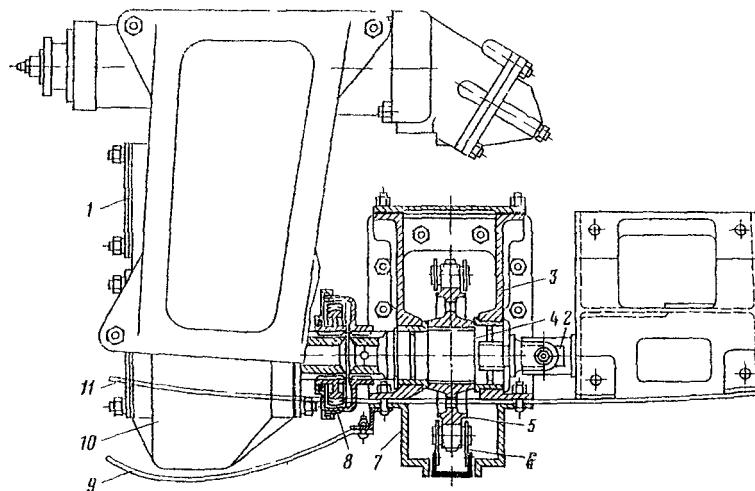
Гидропривод и узел ведущей звездочки тяговой цепи
